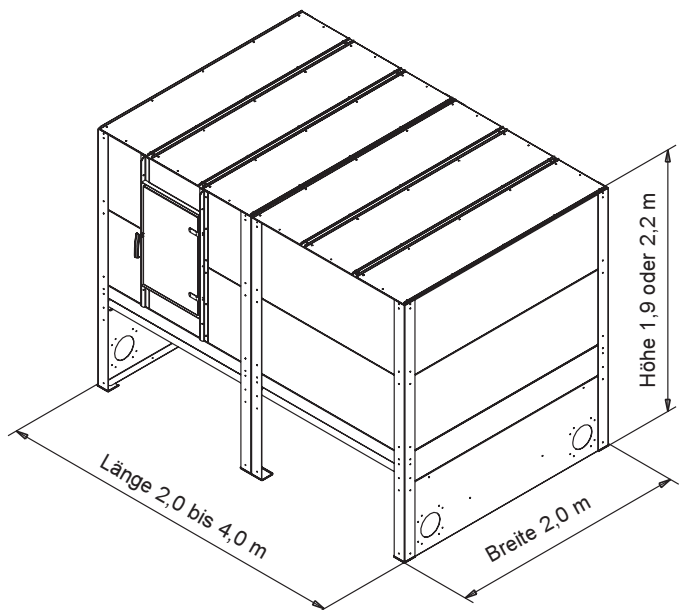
Stahlblech-Tanks mit Breite 2,0 m
